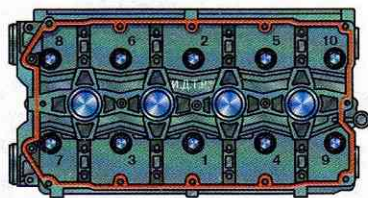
Порядок затяжки болтов крепления головки блока цилиндров
